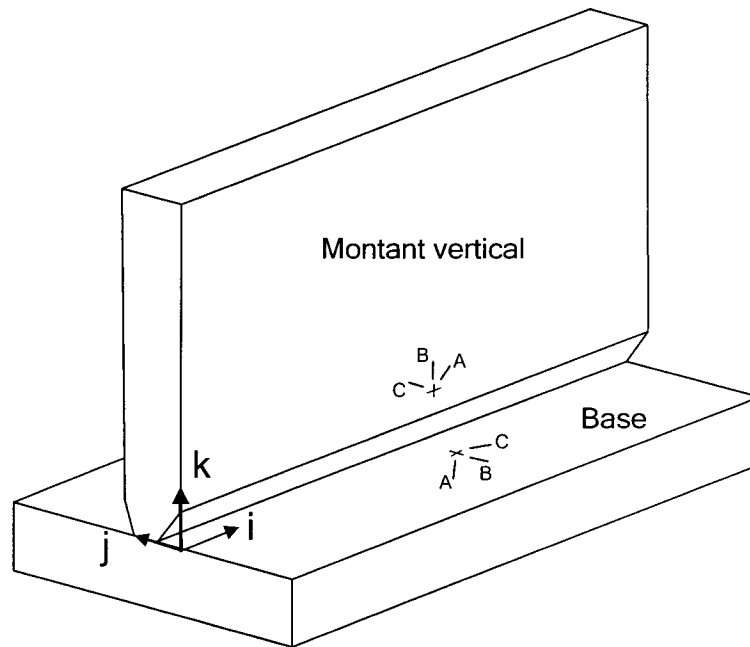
Assemblage des plaques pour le soudage
